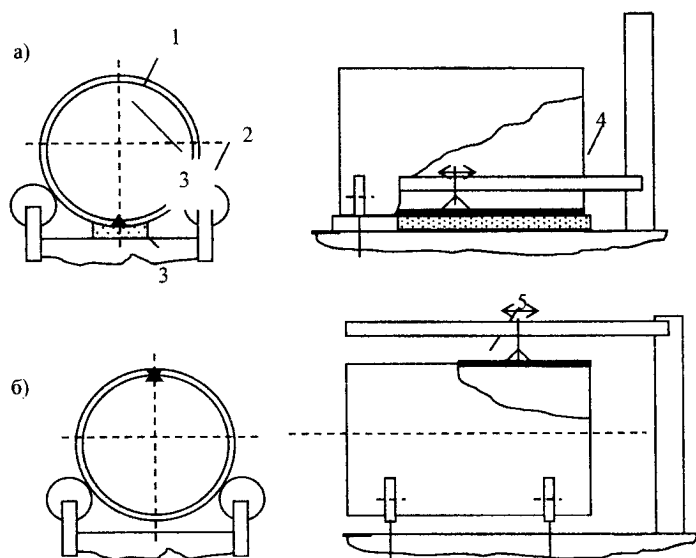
Зварювання поздовжнього шва обичайки.
